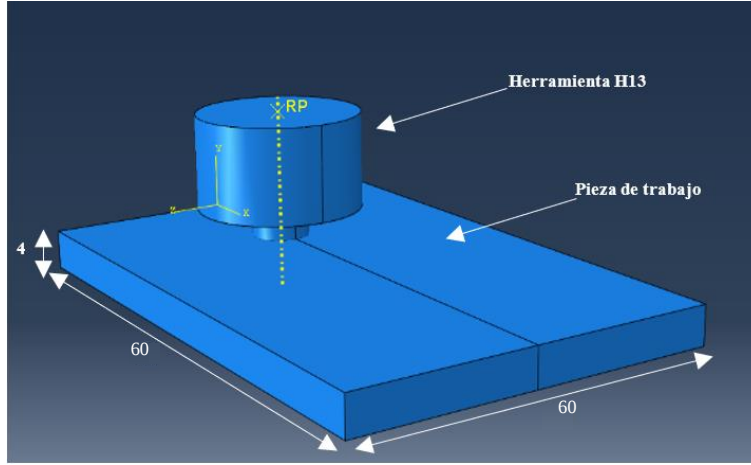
Dimensiones pieza de trabajo (Euleriano) y pieza de referencia.
